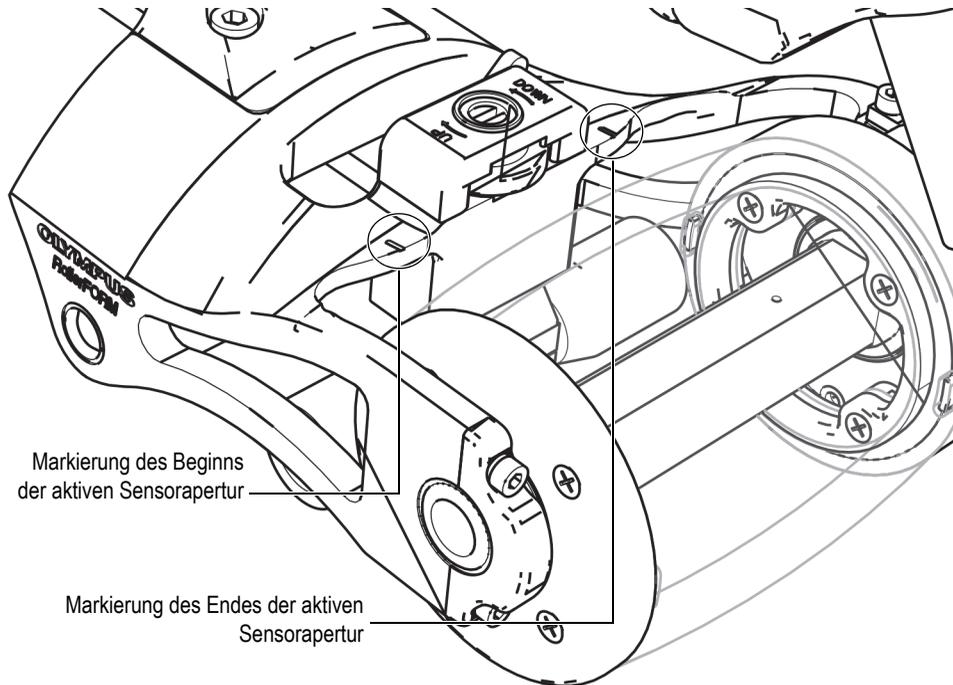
Markierungen oben auf dem Rahmen des RollerFORM
